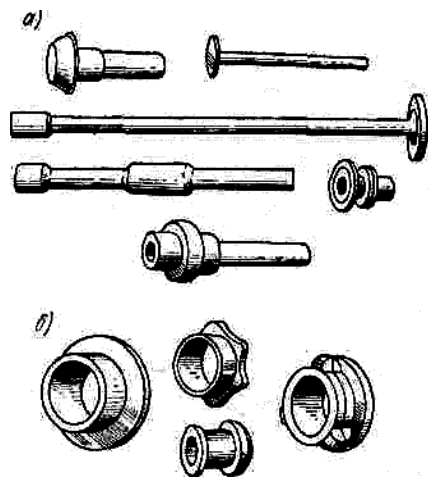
Типовые заготовки, изготавливаемые на горизонтально-ковочных машинах: а-без сквозных отверстий; б - со сквозными отверстиями
